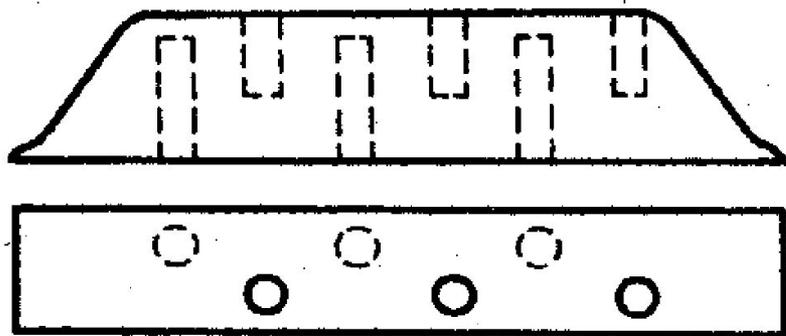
Отбор средней пробы металла или сплава высверливанием
